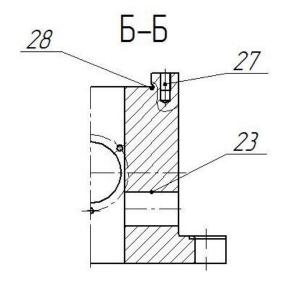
Эскиз корпуса (сечение Б-Б)
